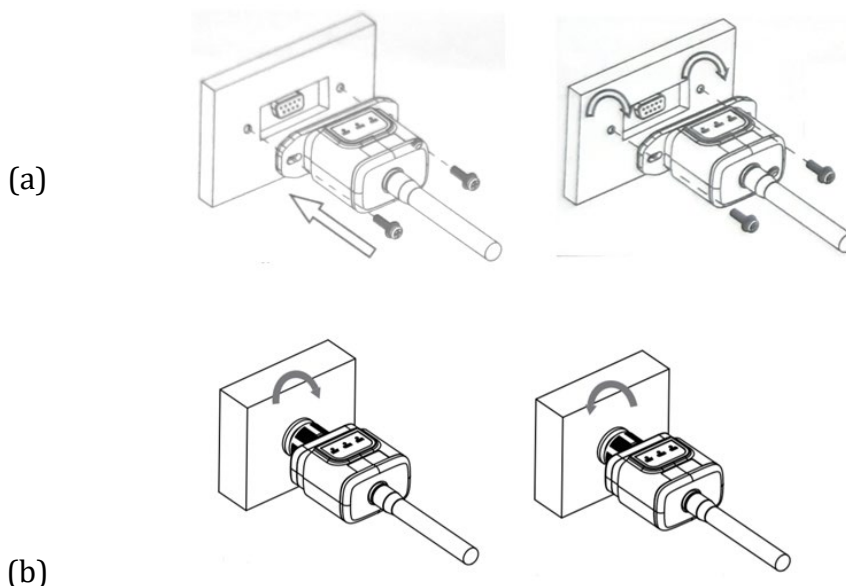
Einschieben und Befestigung der externen WLAN-Platine
